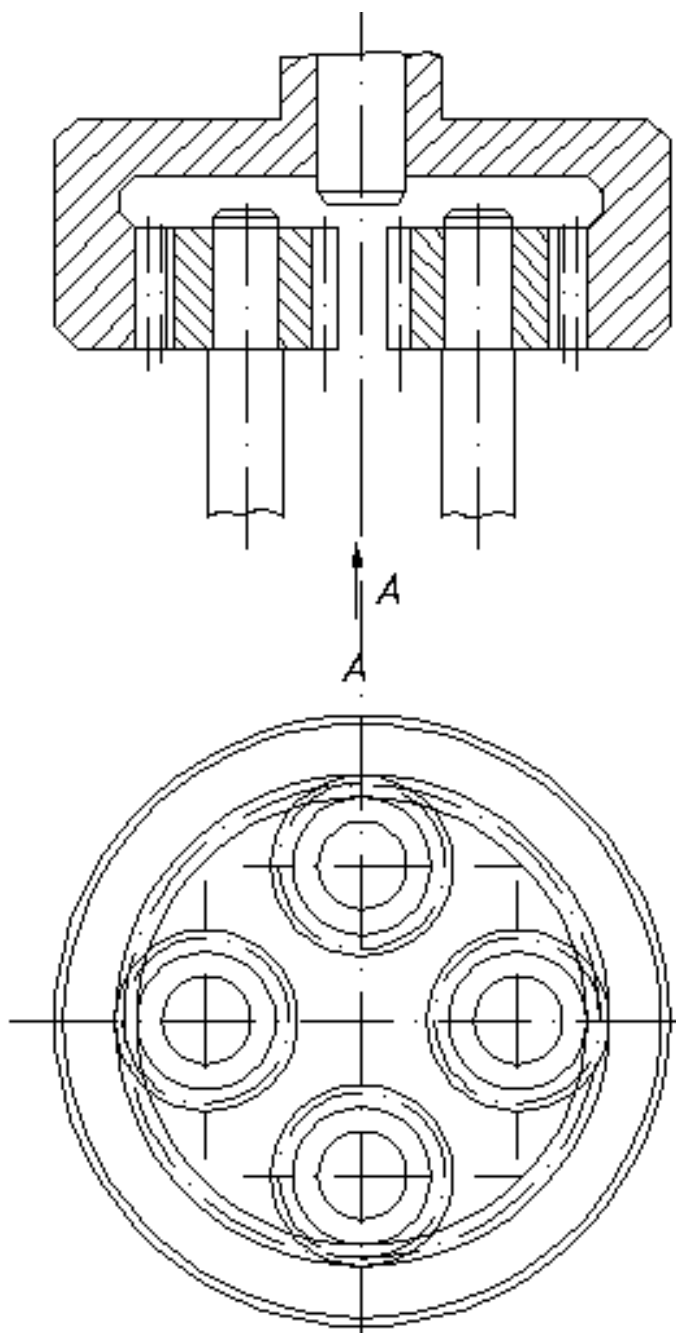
Схема 4-х шпинделів свердильної головки
